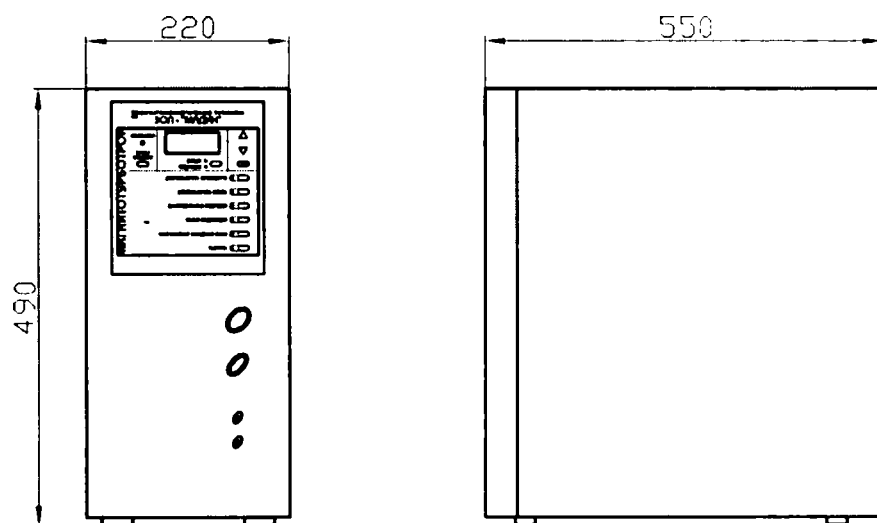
Габаритные размеры генератора установки исполнения Стандарт
